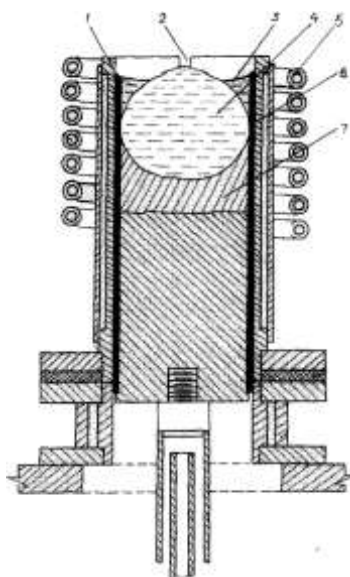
Схема секційного кристалізатора [103]: 1 – секція кристалізатора; 2 зазор; 3 – шлакова ванна; 4 рідкий метал; 5– індуктор; 6–твердий шлак; 7–зливоч
